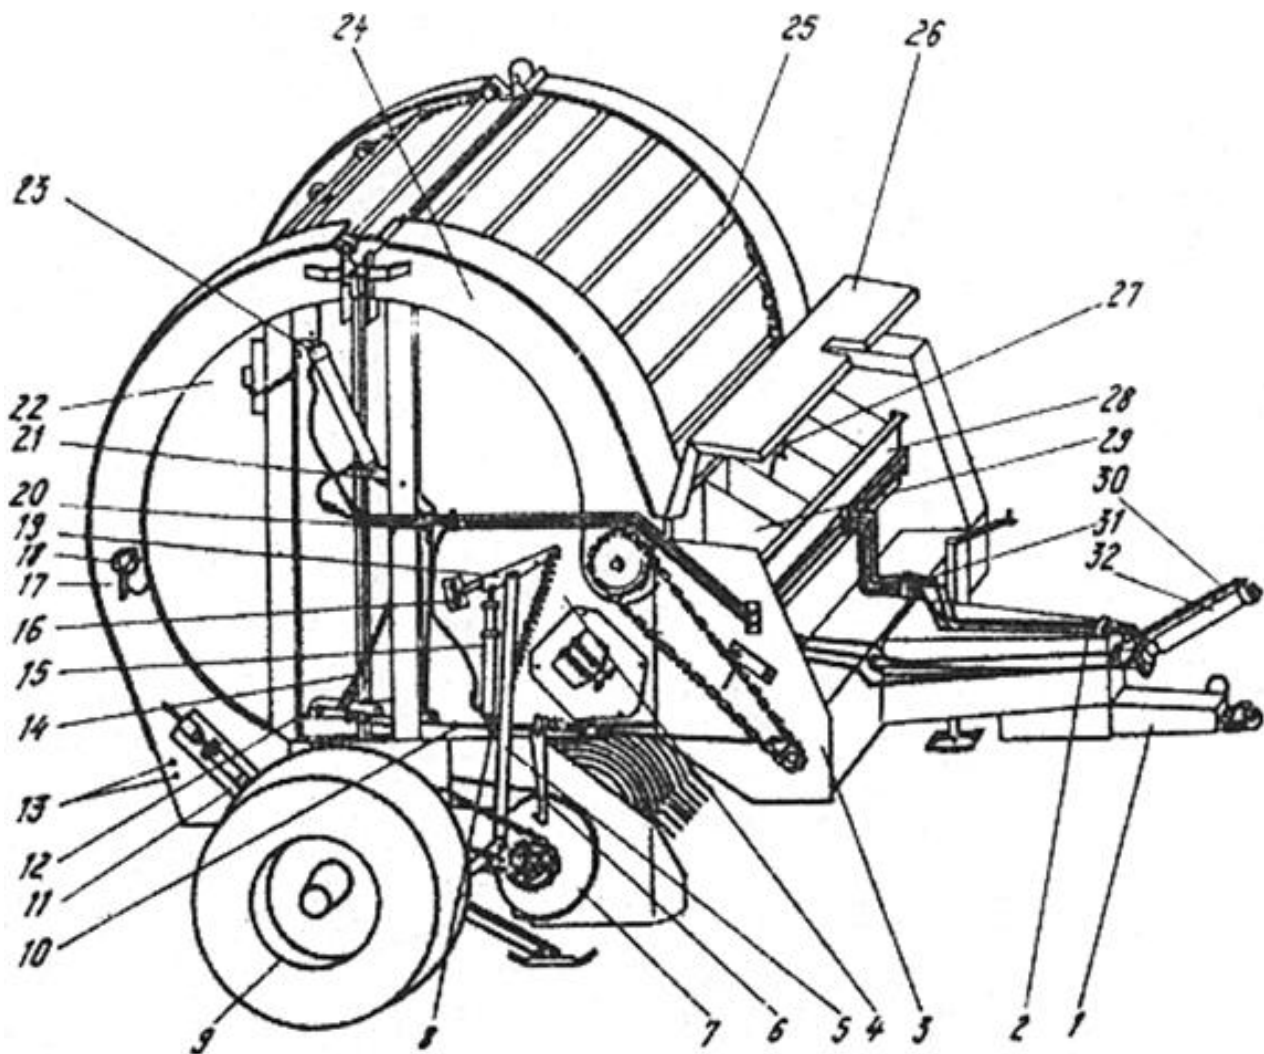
Пресс-подборщик ПР-Ф-750: 1 – сница; 2 – тормозная система; 3 – лобовина; 4 – механизм регулирования плотности прессования; 5 – тяга; 6 – защёлка; 7 – подборщик; 8 – винт; 9 – основание камеры с колёсным ходом; 10 – трос; 11 – натяжная ось; 12 – защёлка; 13 – отверстие; 14 – тяга; 15 – гидроцилиндр; 16 – упор; 17 – кронштейн; 18 – фонарь; 19 – рычаг; 20 – тяга; 21 – рычаг; 22 – задняя часть прессовальной камеры; 23 – гидроцилиндр; 24 – передняя часть прессовальной камеры; 25 – пружина; 26 – крышка ящика; 27 – подпорка; 28 – ящик; 29 – отсек ящика; 30 – трос страховочный; 31 – гидросистема; 32 – карданная передача
